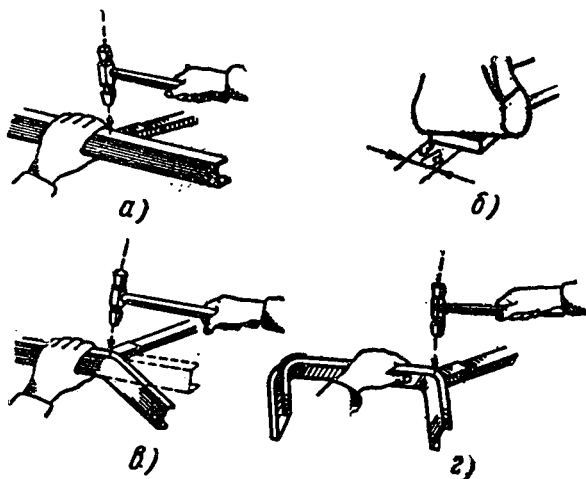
Последовательность изготовления детали разводкой ручным способом:
